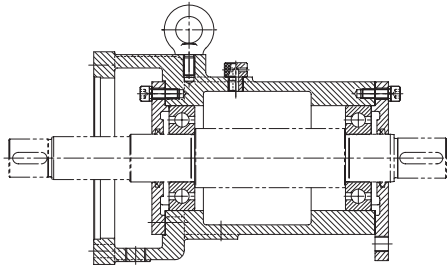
Корпус подшипников с закрытыми подшипниками с постоянной консистентной смазкой
